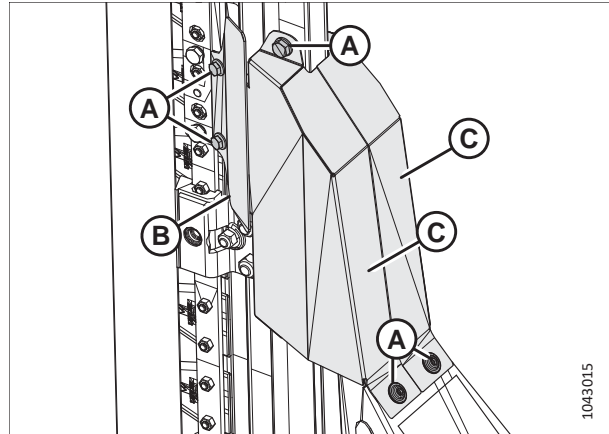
Entfernen der Befestigungselemente um das Messer
